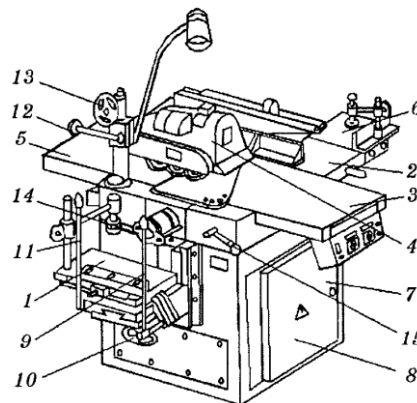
Загальний вигляд комбінованого верстата: 1 – стіл свердлильного агрегату; 2 – стіл пилкового агрегату; 3 – передній стіл фугувального агрегату; 4 – автоподавач заготовок; 5 – стіл задній фугувального агрегату; 6 – каретка для поперечного пиляння; 7 – станина верстата; 8 – електрична шафа; 9 – ручка поздовжньої подачі стола; 10 – маховичок вертикального переміщення стола свердлильного агрегату; 11 – ручка поперечної подачі стола свердлильного агрегату; 12 – ручка фіксування автоподавача; 13 – маховичок для підймання та опускання автоподавача; 14 – свердлильний шпиндель; 15 – ручка для підймання та опускання переднього стола фугувального агрегату
